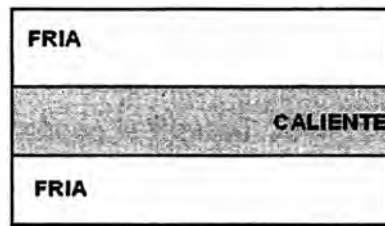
Calentamiento local producido durante la soldadura de dos placas.
